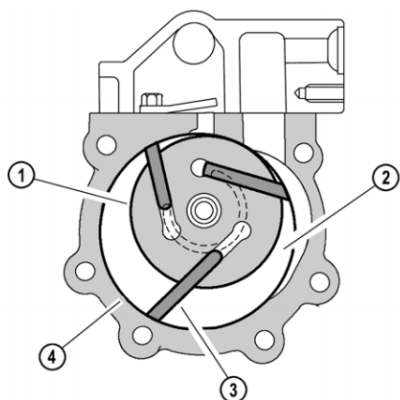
Лопастный компрессор или компрессор роторного типа:
